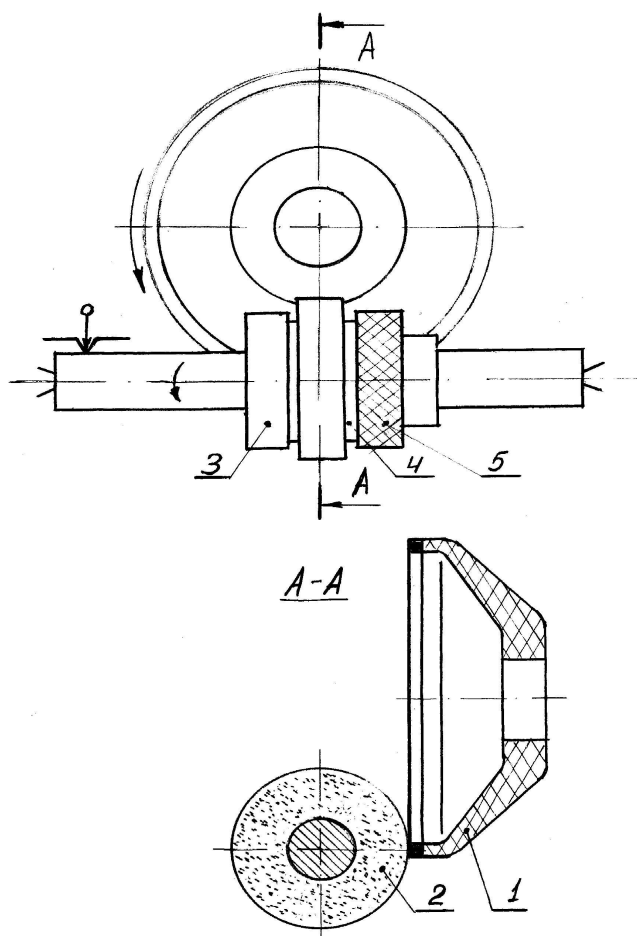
Схема доводки ролика торцом круга на станке модели 3В642: 1 — алмазный круг 12А2-45° 80x20x3x3 АСМ 28/20 4 ЭЗ; 2 — ролик твердого сплава; 3 — оправка; 4 — шайба; 5 — гайка
